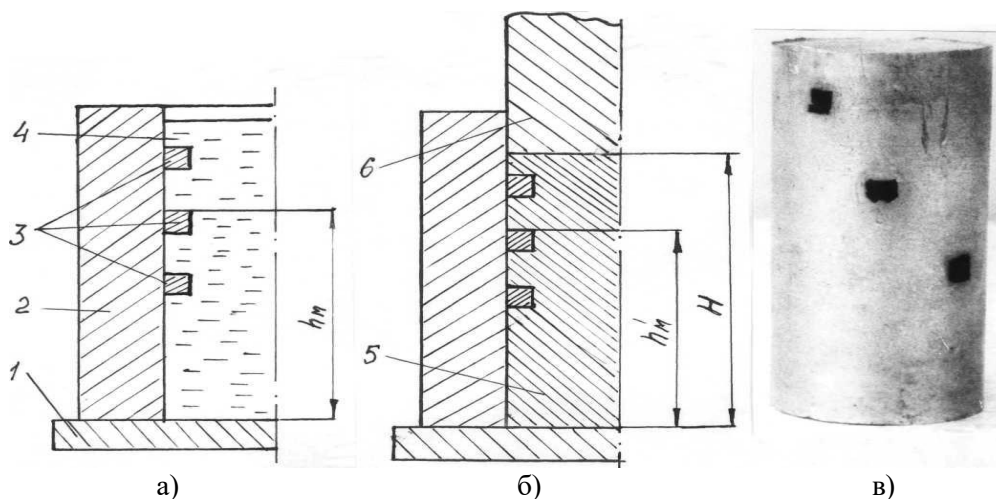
Схемы установки постоянных магнитов по высоте матрицы до заливки расплава в матрицу (а) и их расположения в отливке (б); в – отливка со стержнями - магнитами
